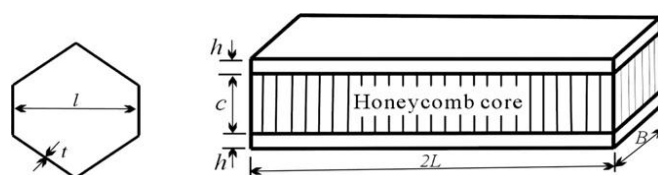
geometria e dimensioni dei sandwich con cuore in struttura honeycomb [52].
